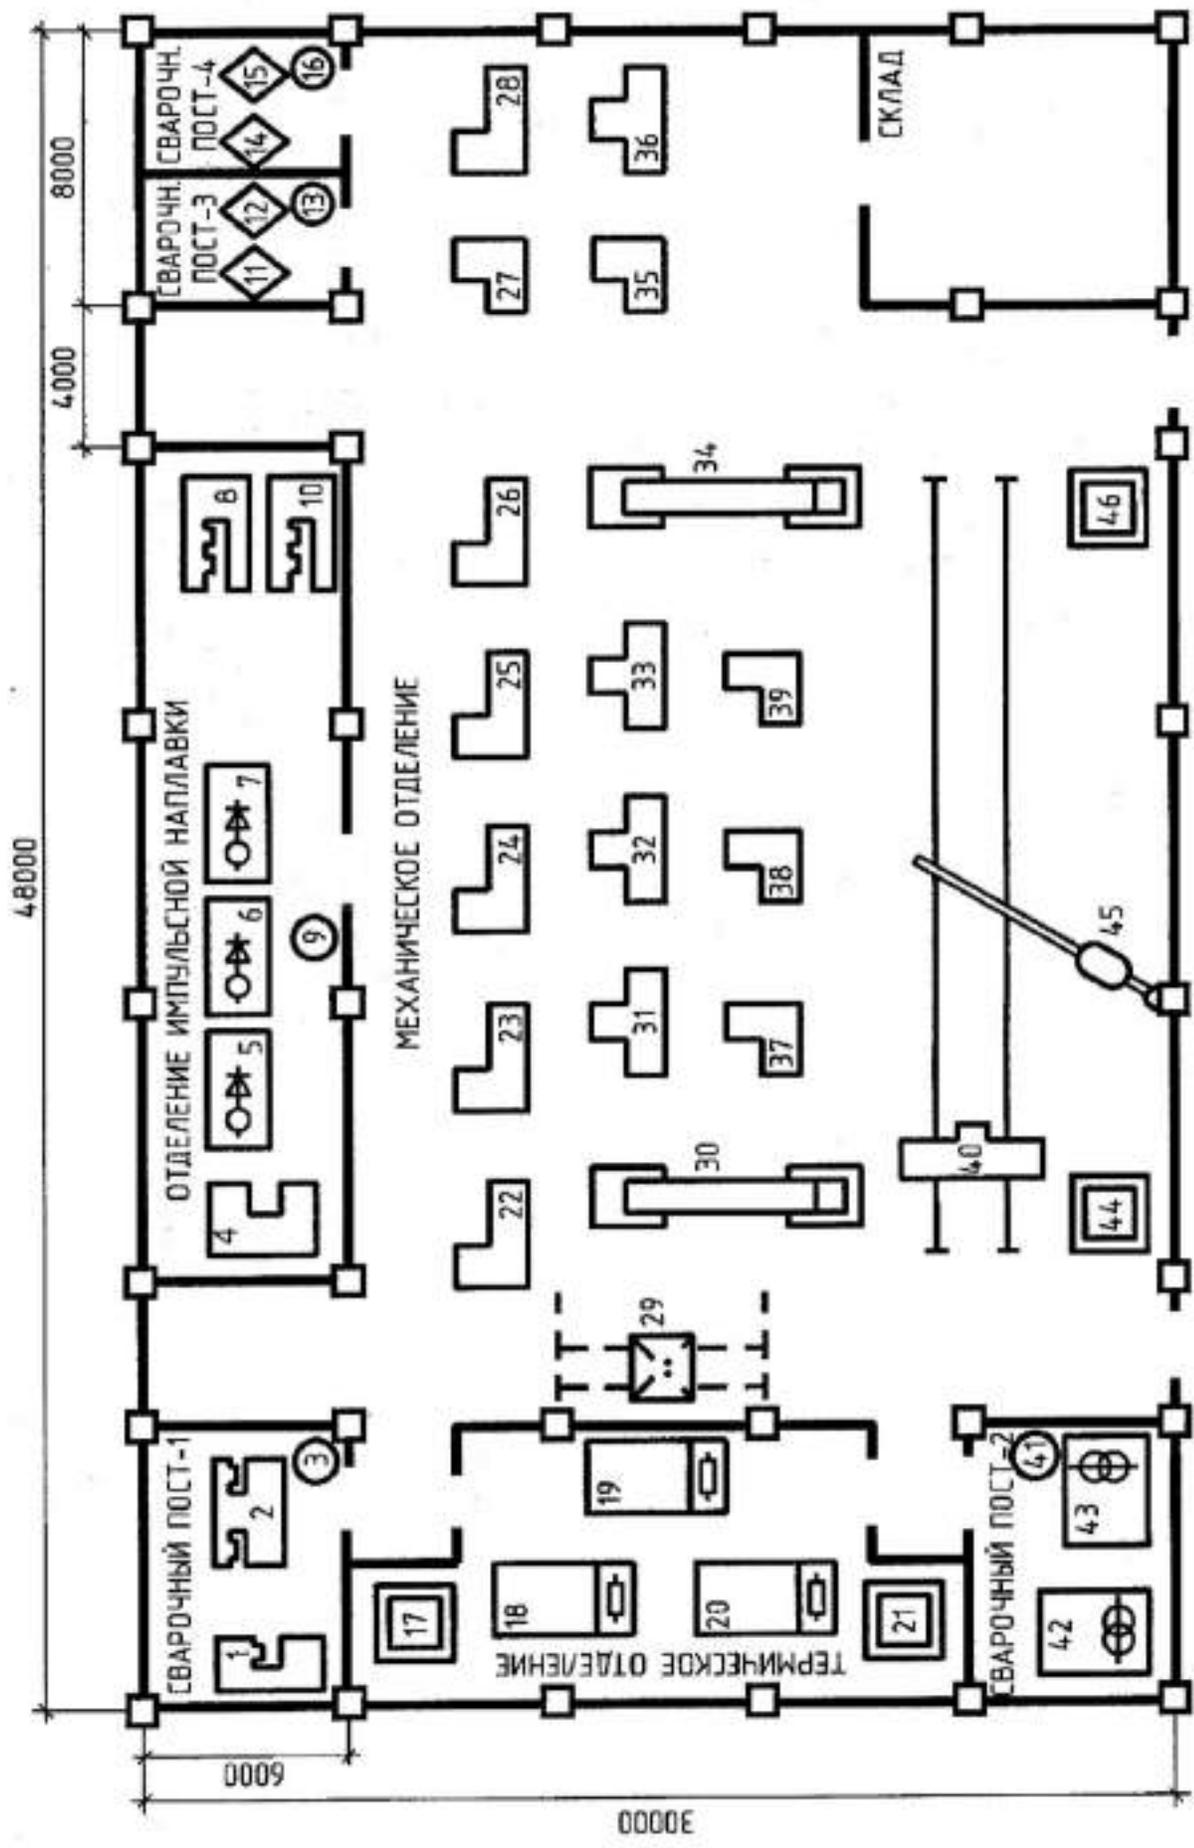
План расположения ЭО сварочного участка цеха
